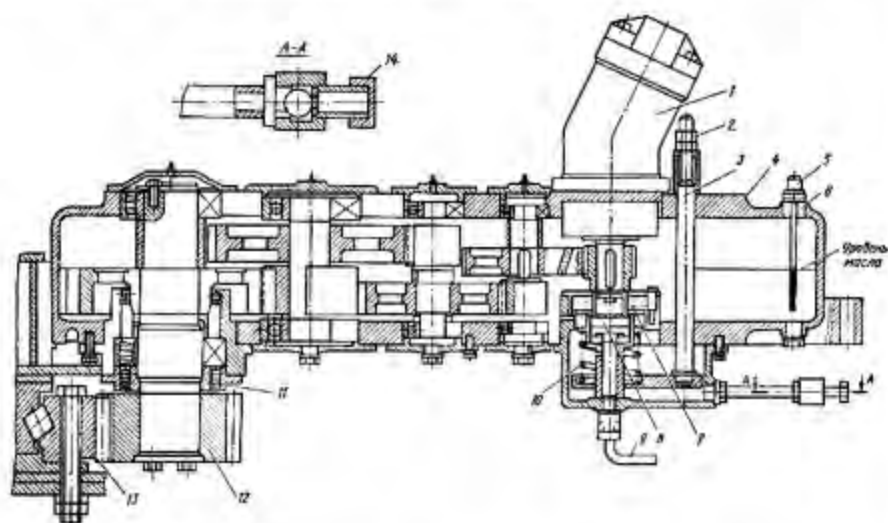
Механизм поворота крана КС - 6471. 1 - гидромотор, 2, 14 - гайка, 3 - шток, 4 - вертикальный редуктор, 5 - щуп, 6 - пробка-щуп, 7 -
